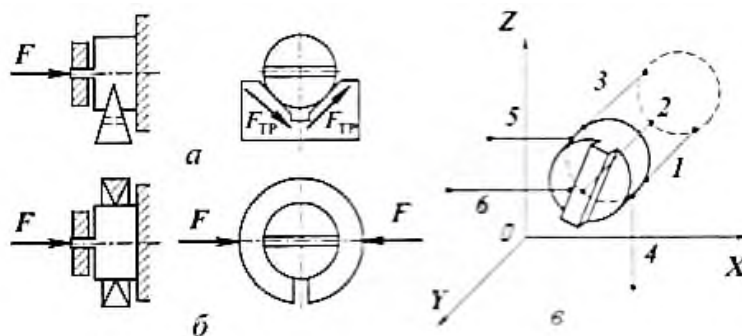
Базирование и закрепление короткого цилиндрического тела [8]
